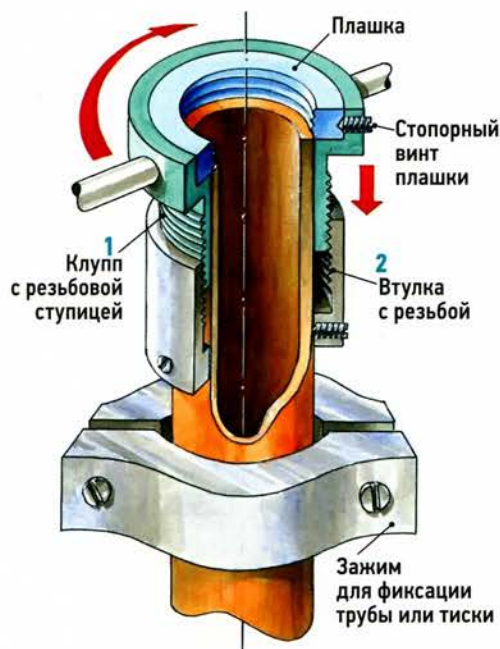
Первый вариант приспособления для нарезания резьбы на металлических трубах.
